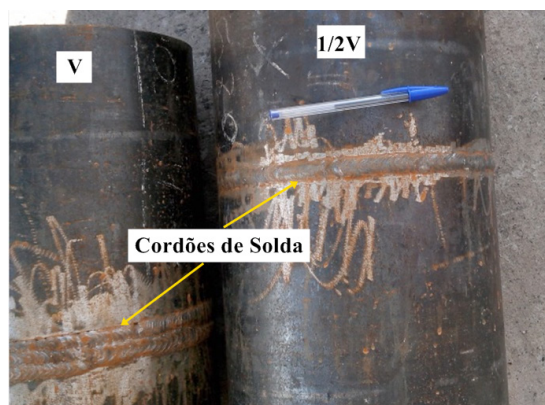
Fotografia do material como soldado: juntas soldadas com chanfro V e ½ V.
